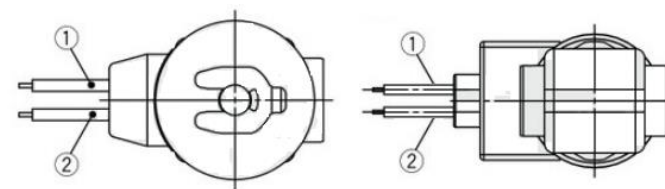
Eingegossenes Kabel und eingegossenes Kabel mit PCB
